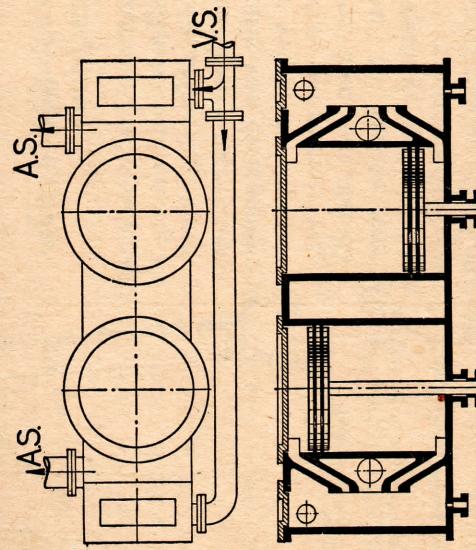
Dubbele, enkelvoudige expansiemachine.
